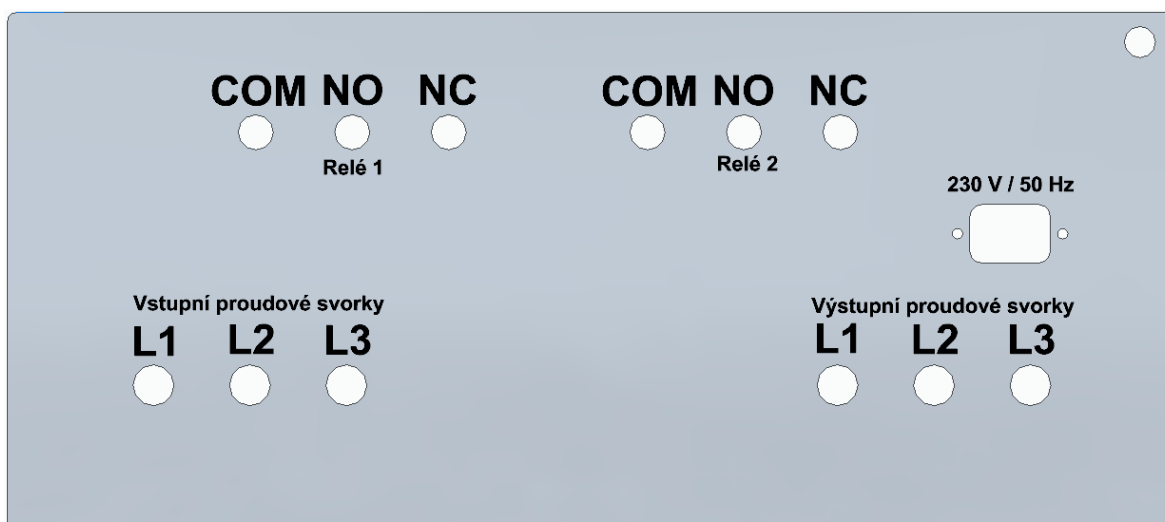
Technická dokumentace pro úpravy spodní strany.
